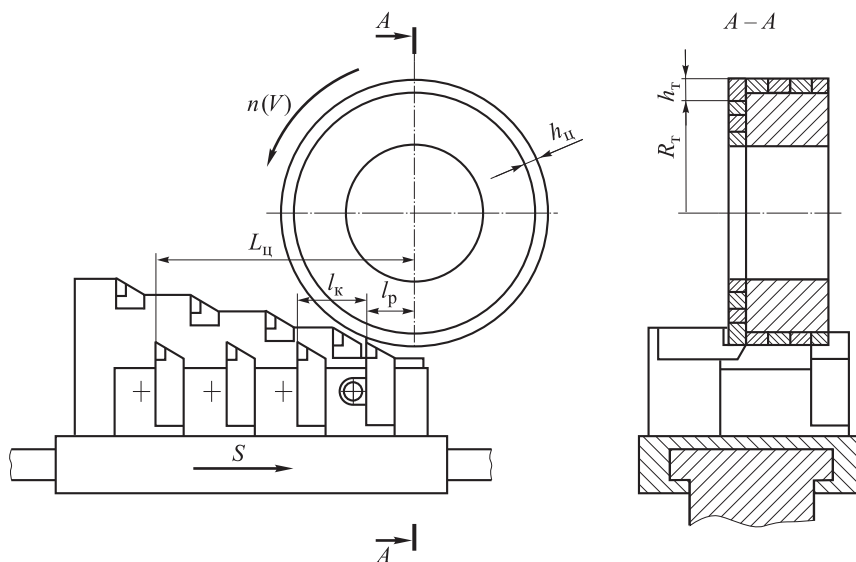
Схема ПТТ наружной цилиндрической и торцевой поверхности с прямолинейной подачей инструмента:
